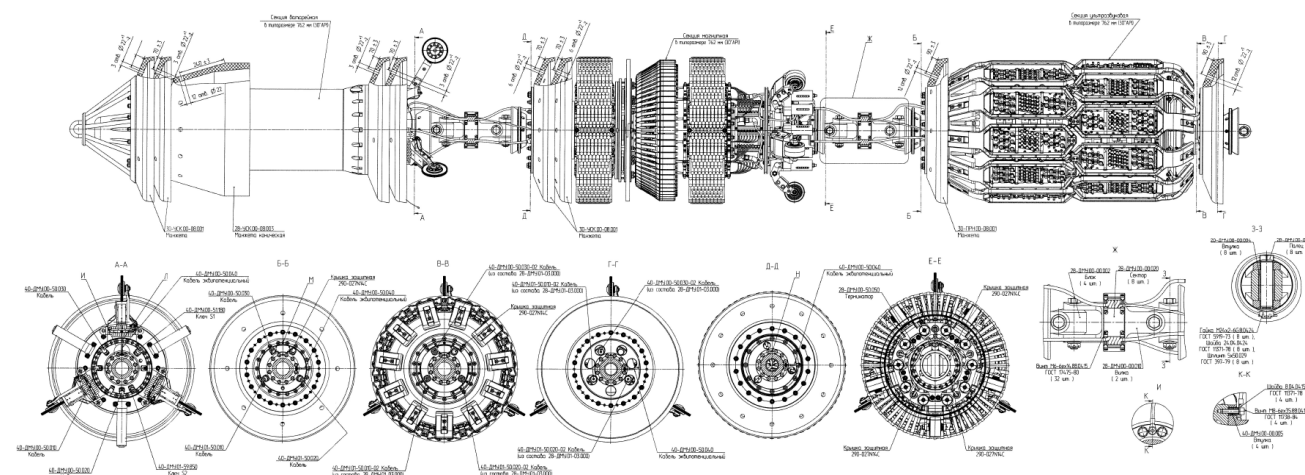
Чертеж общего вида дефектоскопа внутритрубного комбинированного магнитно-ультразвукового 28-ДМУ.01-00.000 в типоразмере 762 мм (30" API)
